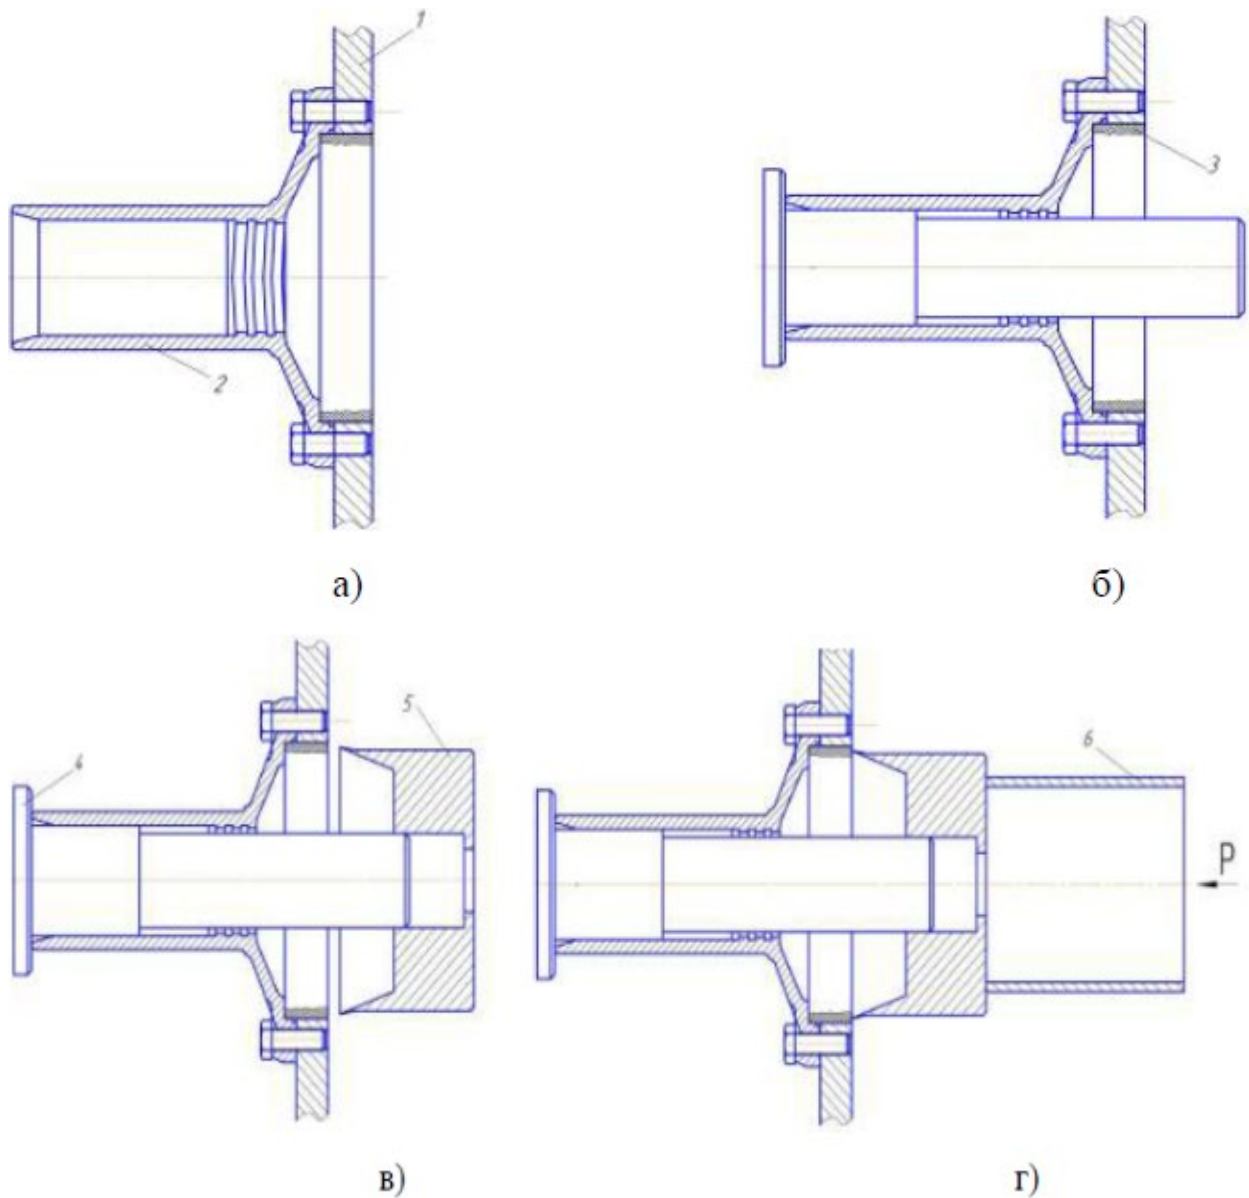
Схема послідовності етапів отримання отвору з полімерним покриттям у корпусній деталі (корпус коробки передач, водяного насоса двигуна) калібруванням:
